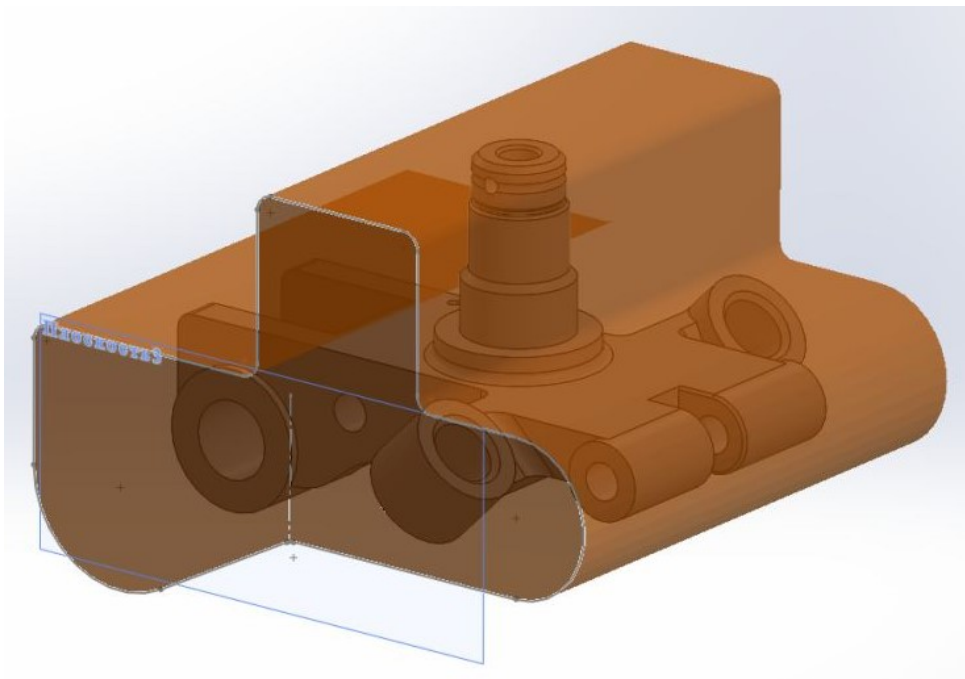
Тривимірна модель заготовки деталі напіввісь.
